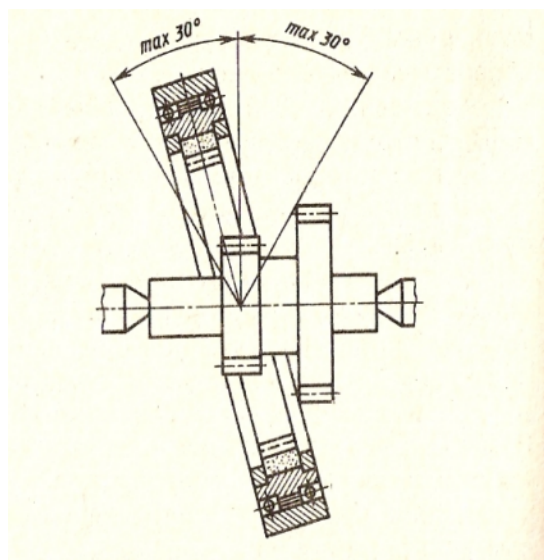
Схема хонингования зубчатого колеса хонем с внутренними зубьями
